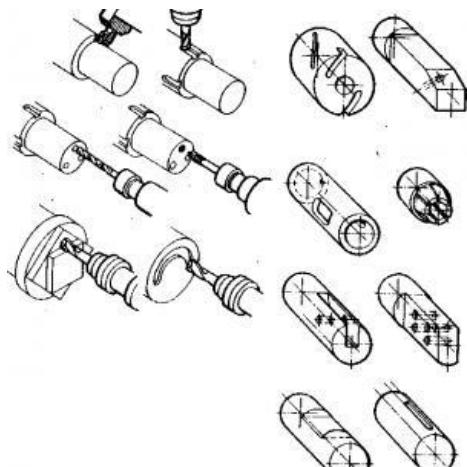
Примеры обработки на станках с револьверной головкой с приводными шпинделами
